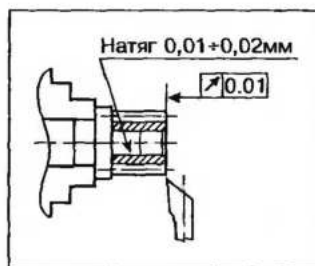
Обработка торца шестерни масляного насоса на токарном станке
